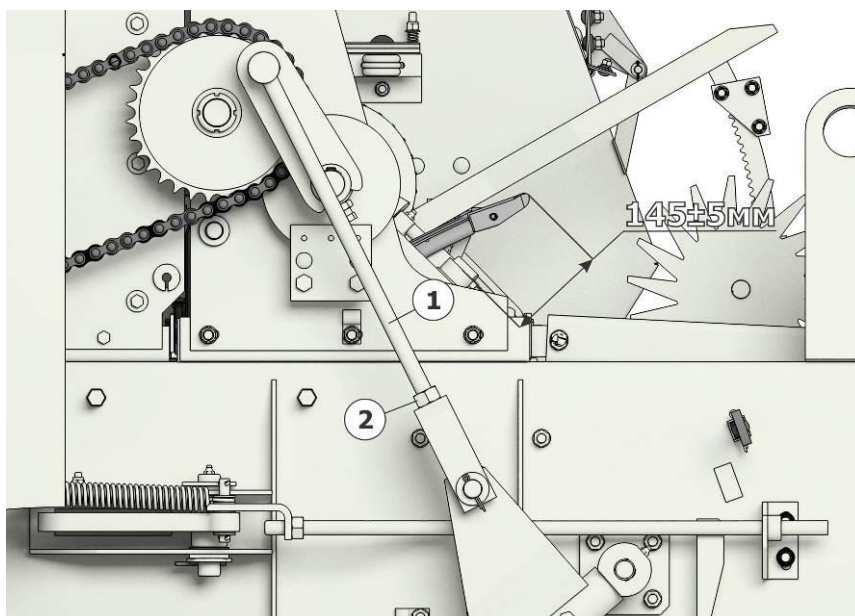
Регулировка положения зубчатого колеса обвязывающего узла
